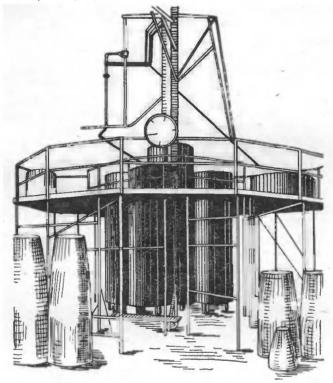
Центробежная формовочная машина для изготовления труб из стеклопластиков.
